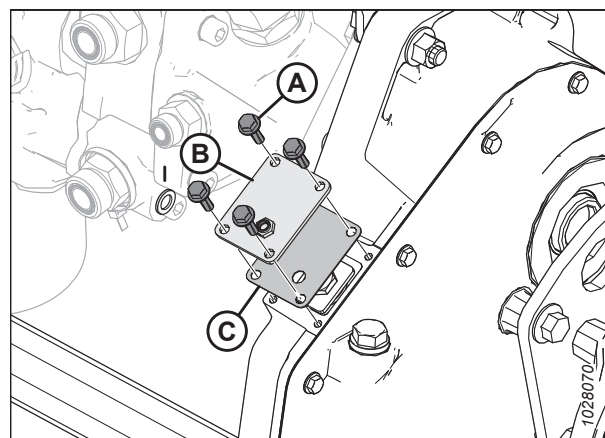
Hauptgetriebe mit Kettenspannerabdeckung
